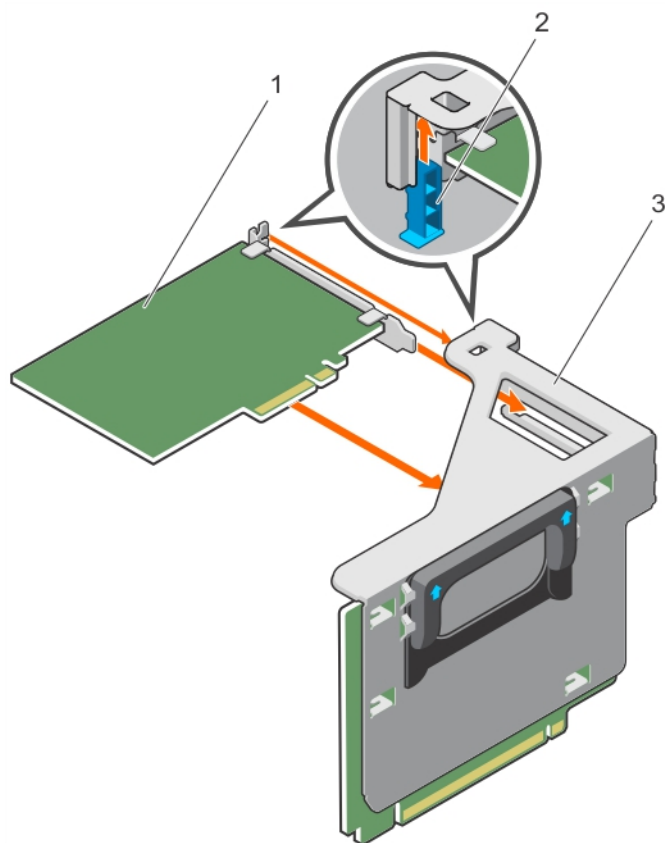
Installation de la carte d'extension (demi-longueur) à partir de la carte de montage pour carte d'extension gauche
